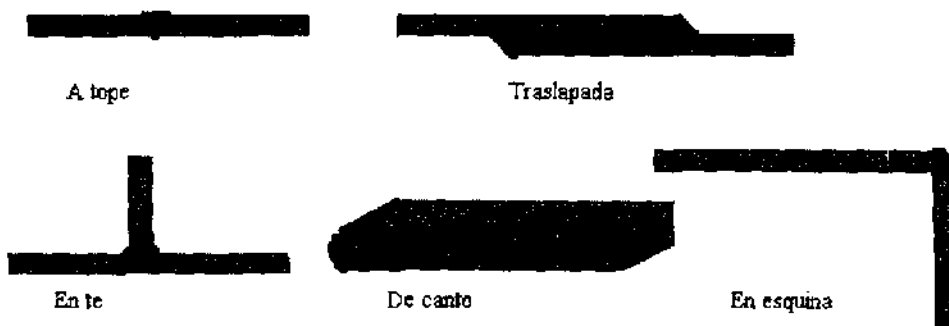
Soldaduras de acuerdo al tipo de junta.
